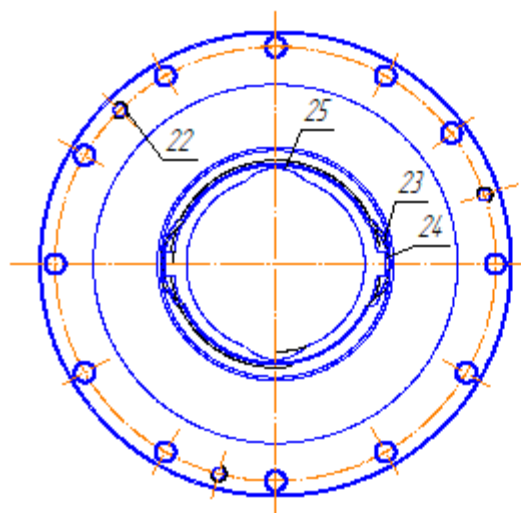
Ескіз деталі с нумерацією поверхонь
